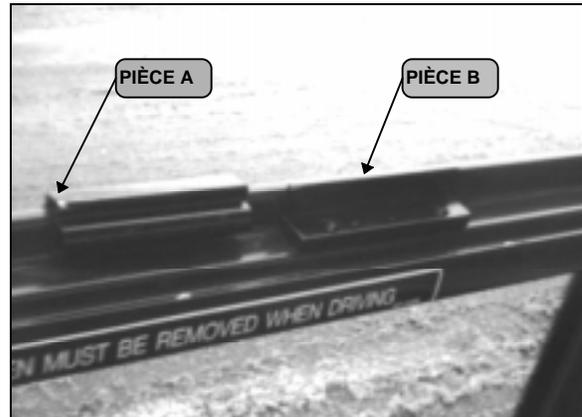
INSTALLATION DE LA NOUVELLE PIÈCE (PIÈCE B)
